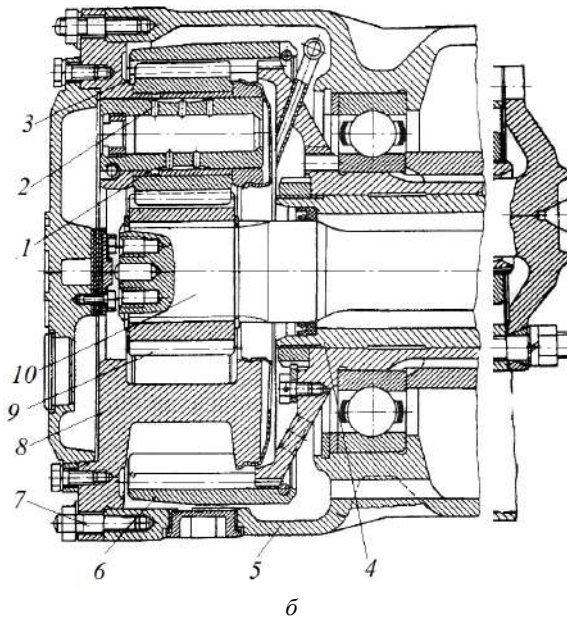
Борговий редуктор із внутрішнім зачепленням:
